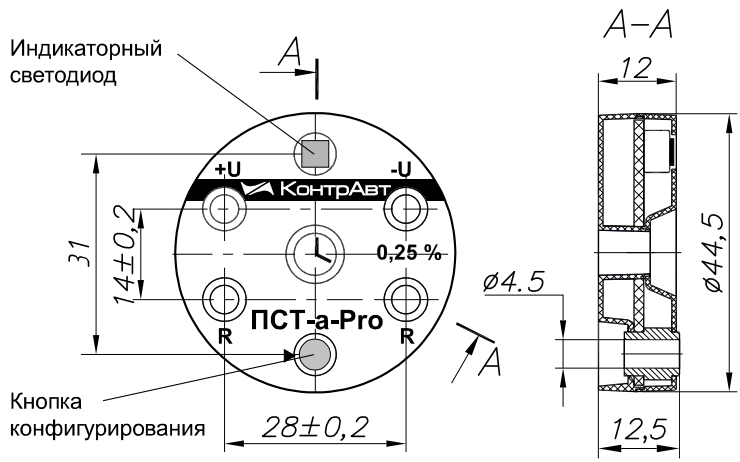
Внешний вид и габариты преобразователя ПСТ-а-Pro-M0
